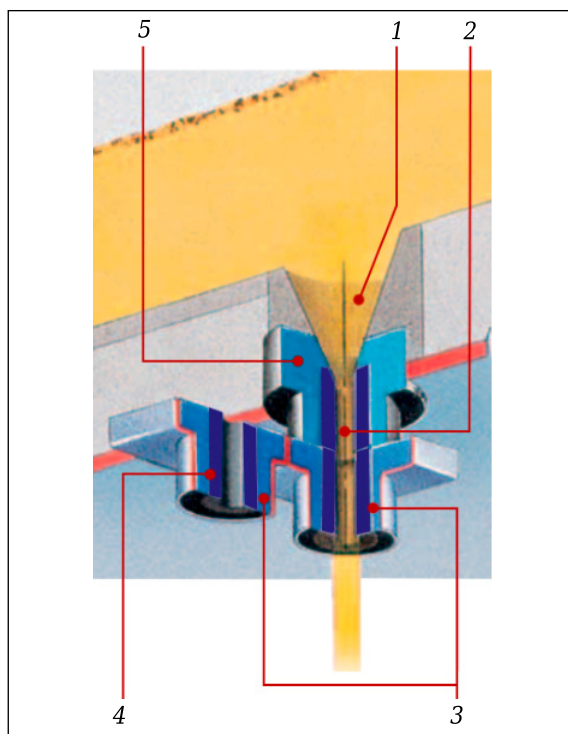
Принципиальная схема быстрой смены стаканов-дозаторов промежуточного ковша сортовой МНЛЗ: 1 — воронка из набивной массы или формованный гнездовой блок; 2 — калиброванная струя металла; 3 — нижний (сменный) стакан-дозатор; 4 — ZrO_2 -вставка стакана-дозатора; 5 — верхний стакан-дозатор типовой конструкции
